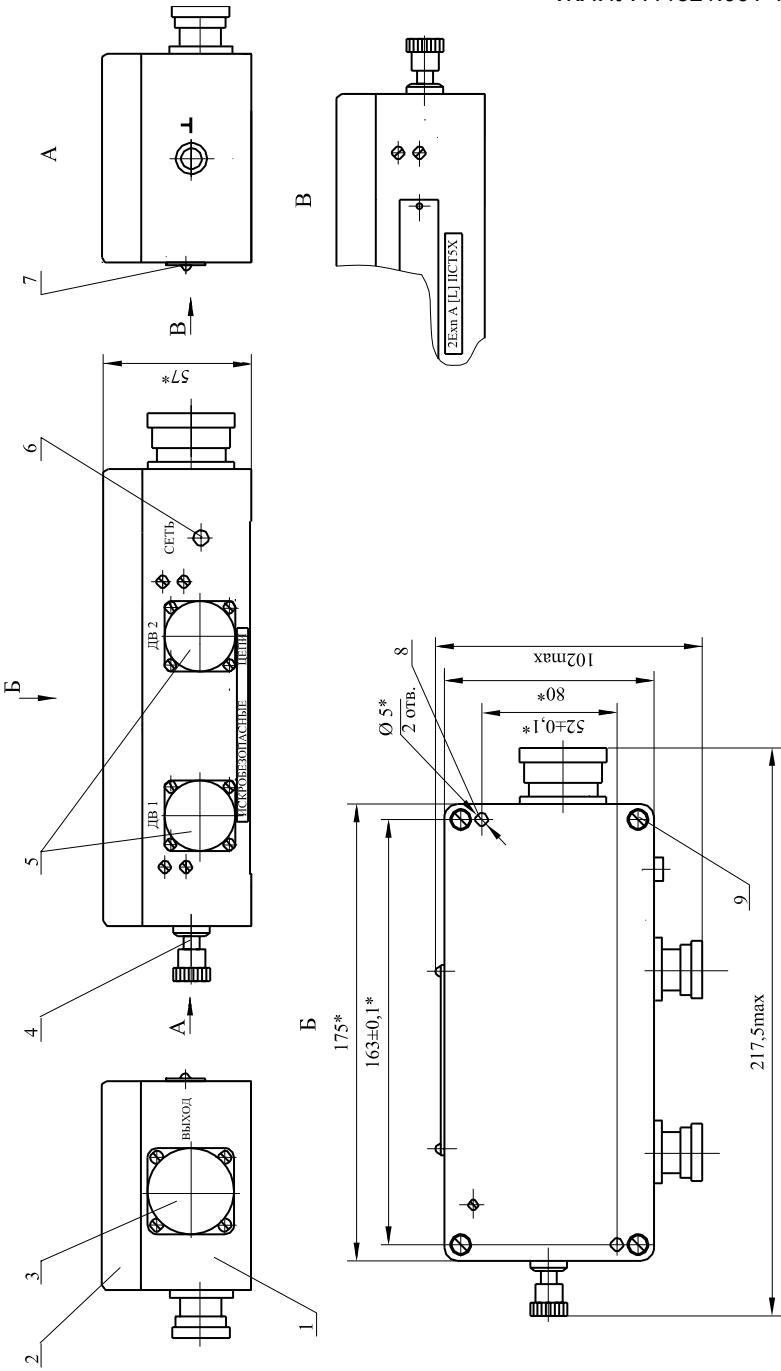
(1 из 2) - Габаритно - установочные размеры согласующего блока БС-16-17В
